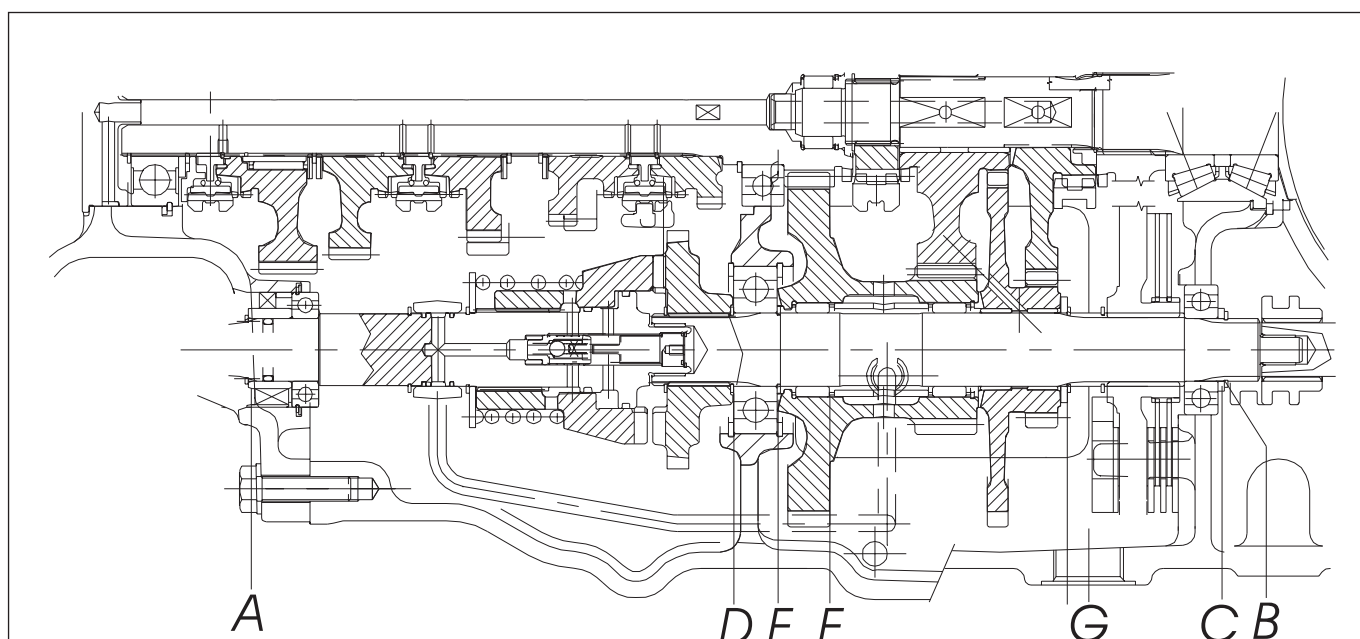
Ensemble de prise de force pour les roues motrices avant.
